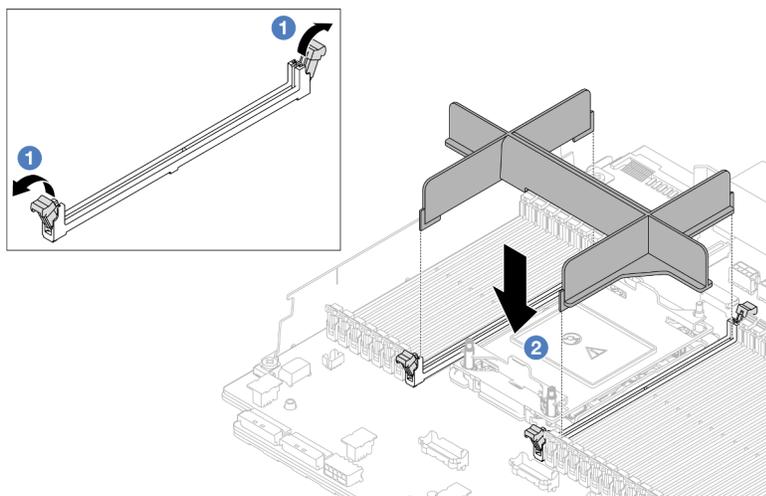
Installation d'un obturateur de module de processeur-dissipateur thermique
